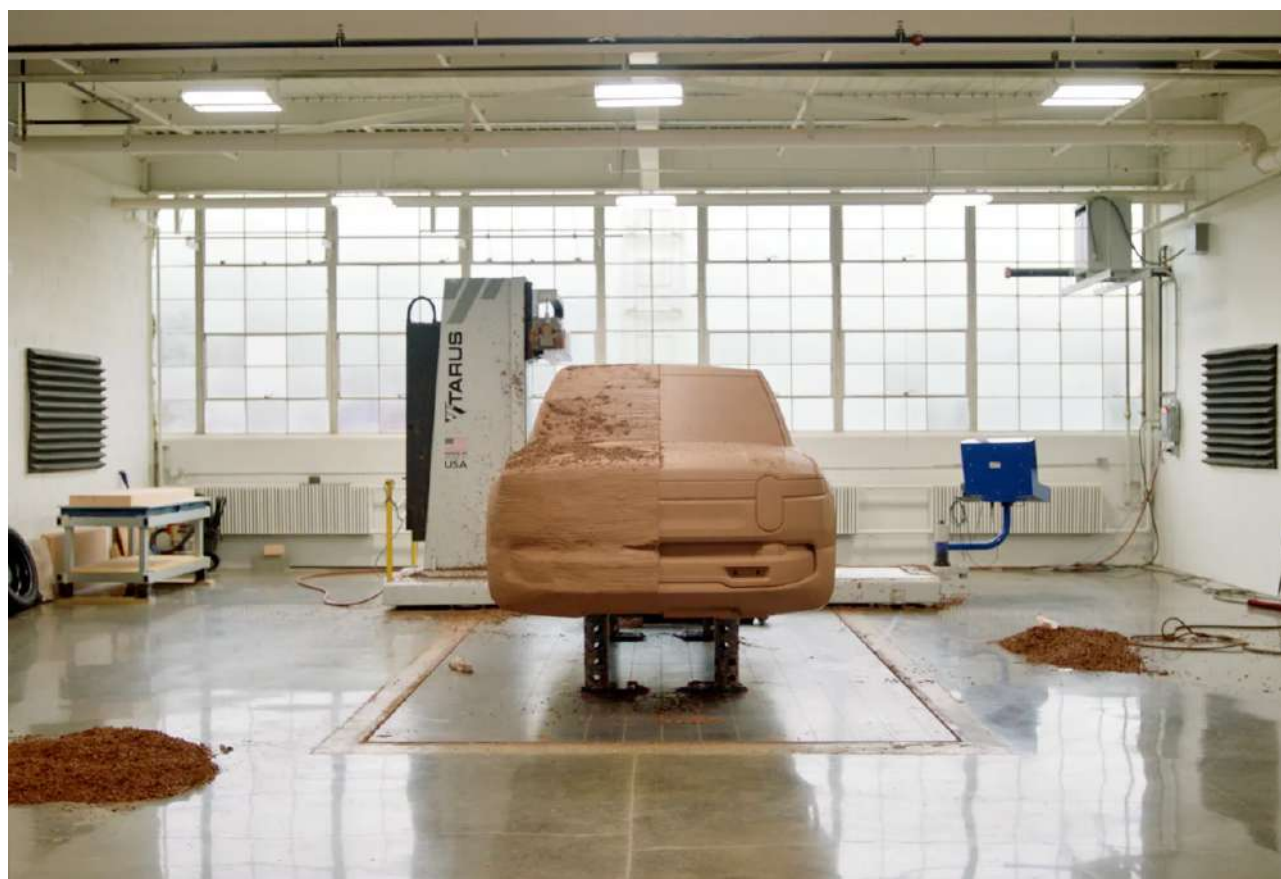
CNC de 5 eixos usinando modelo de aparência de carro. Fonte: <https://claymill.com/>
